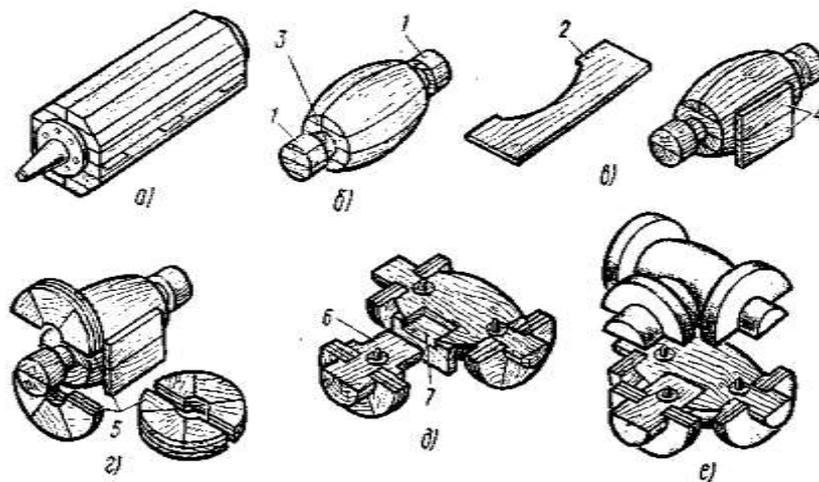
Последовательность обработки и сборки модели корпуса вентиля.
